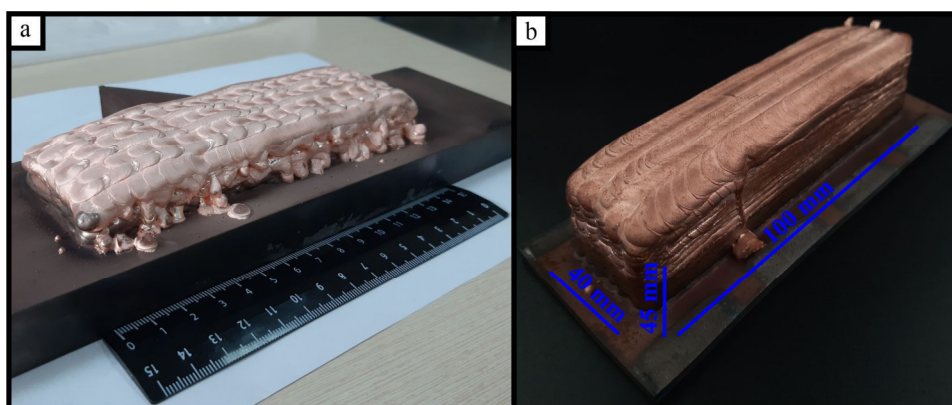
Внешний вид образцов, полученных с реализацией в процессе печати капельного режима (а) и нестабильного струйного режима (б)
